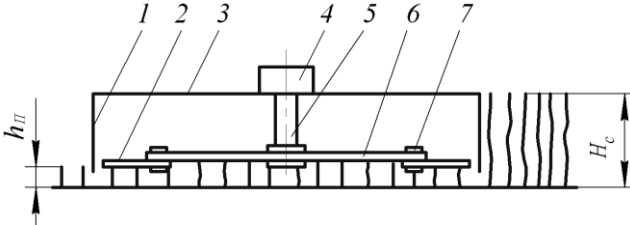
Схема різального апарату подрібнювача-розподільовача з дисковим робочим органом: 1-обичайка; 2-ніж; 3-кожух; 4-редуктор; 5-вал; 6-тримач; 7-шарнір
